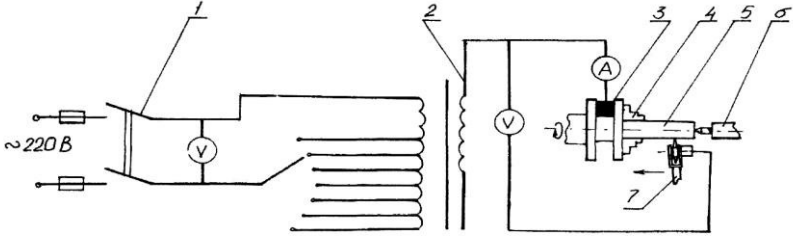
Принципова схема електромеханічної обробки деталі на токарному верстаті:
